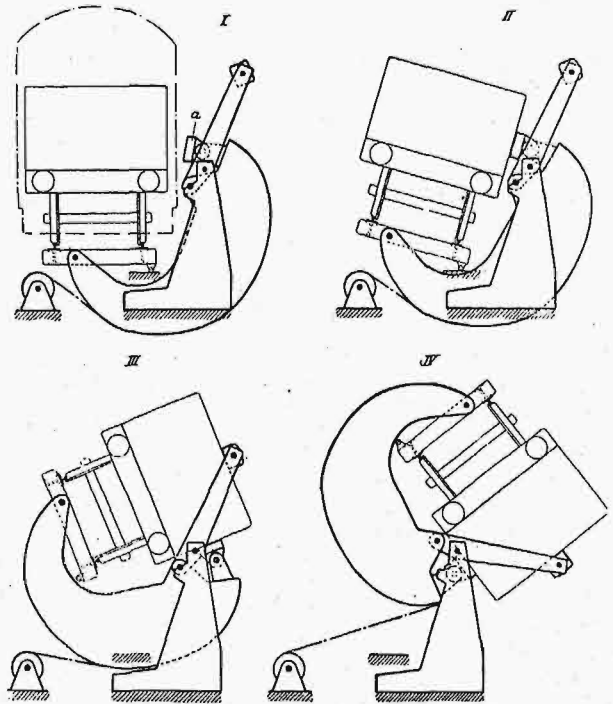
i 6. Wywrotnik boczny bud. Mitchell Conveyor Transporter Co.
